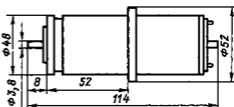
29 Габаритные и установочные размеры двигатель-генератора АДГ-124Б
